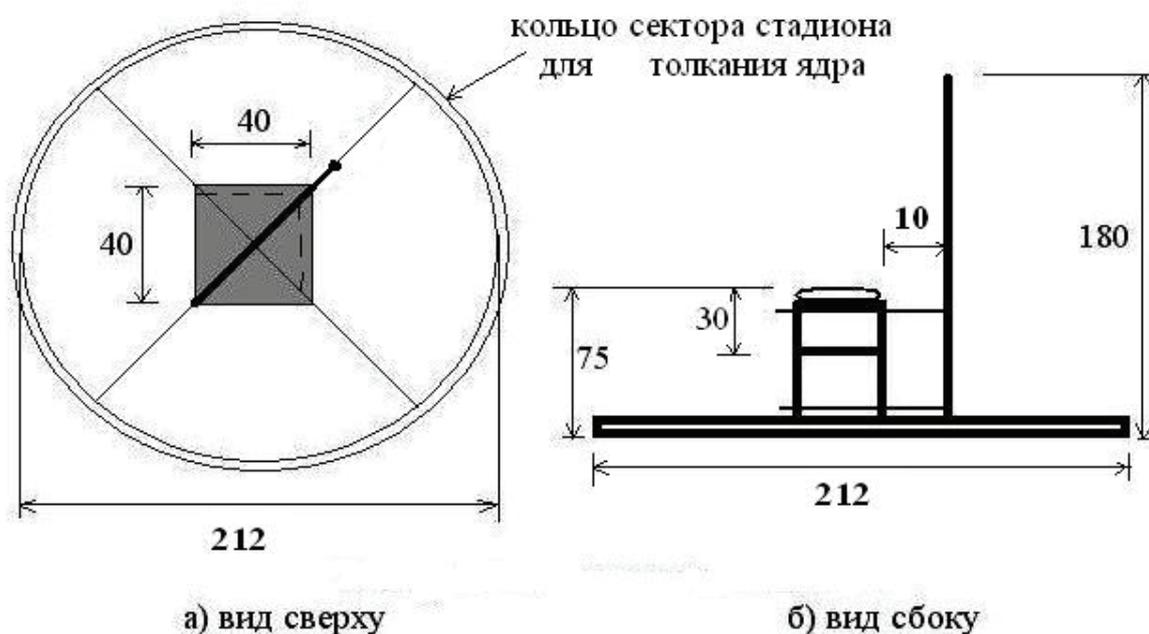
Универсальный станок для метаний (размеры даны в см)
